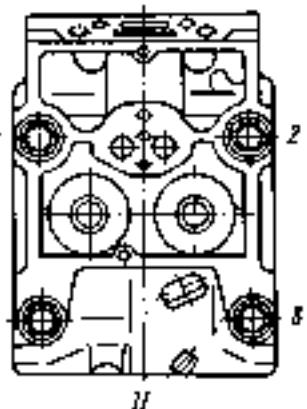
Reihenfolge, in der die Schrauben zur Befestigung des Zylinderkopfes angezogen werden:
